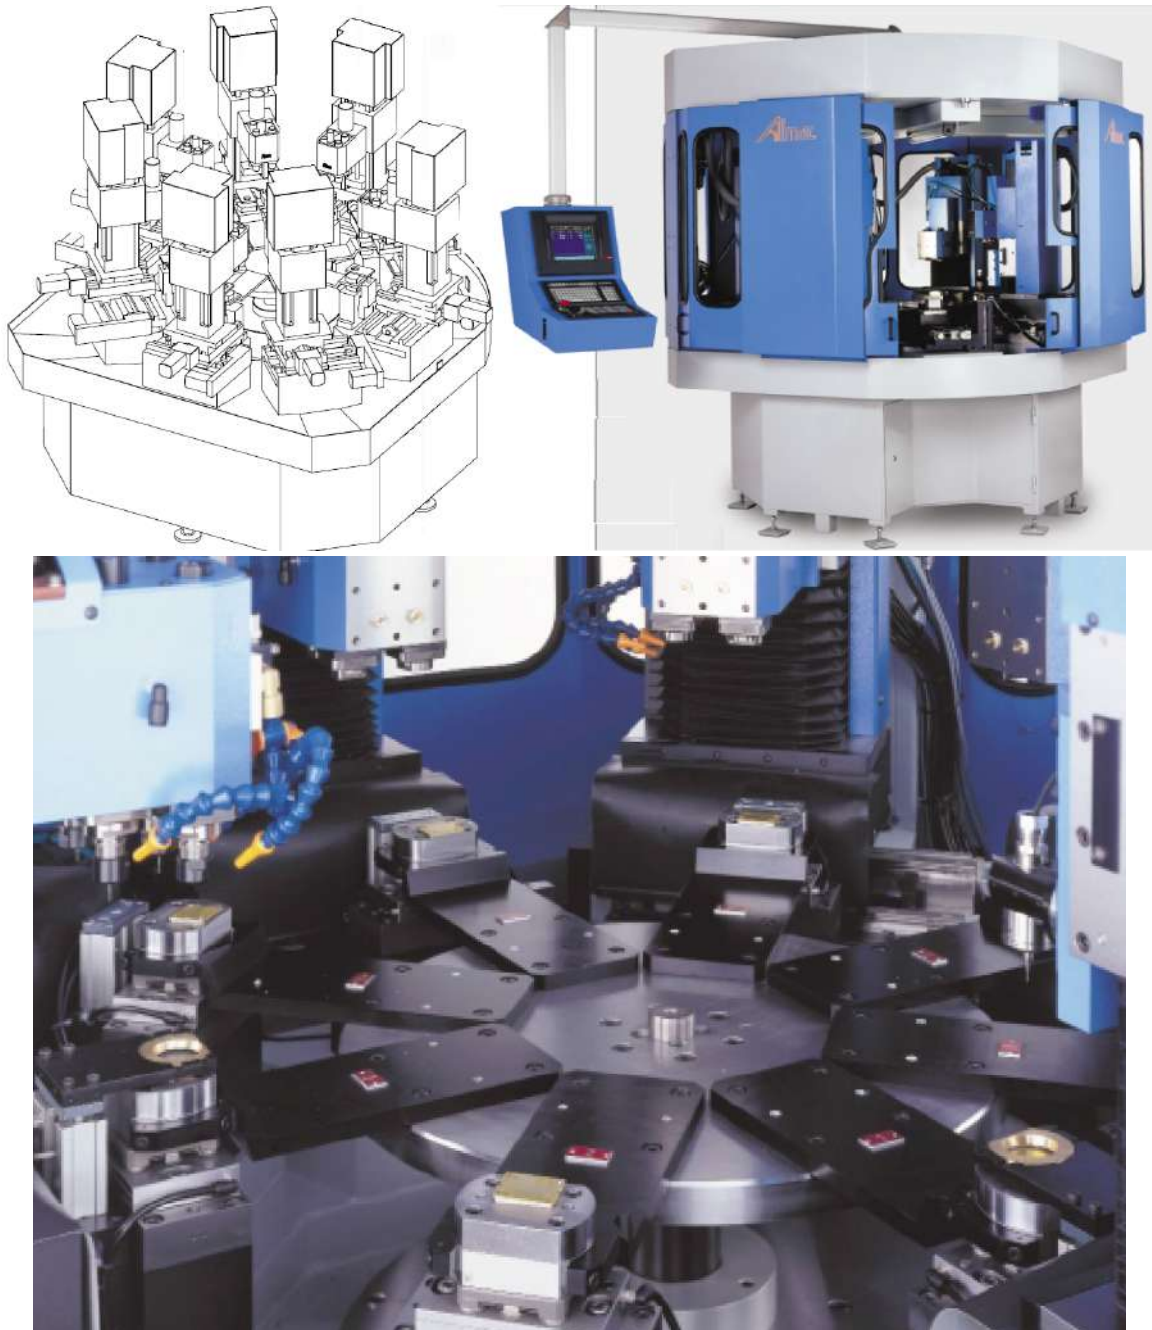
Компонування а грегатного верстата з поворотно-розподільчим столом ALMAC MCT 644
